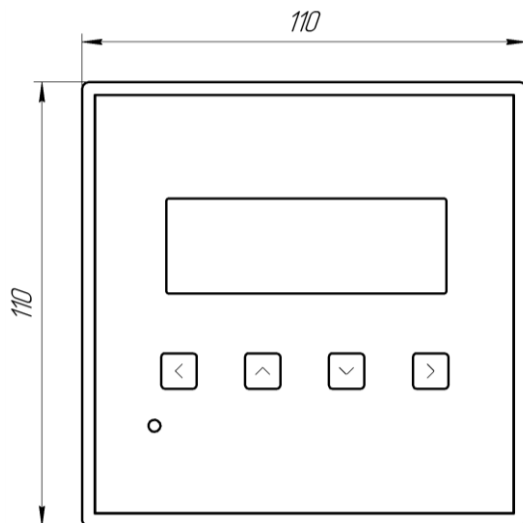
Габаритный чертеж измерителя MI-xAC (вид спереди)
